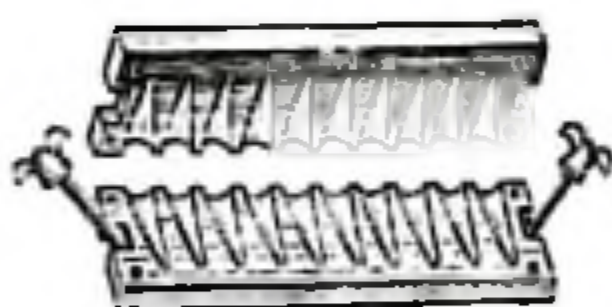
Фрезерованная форма для отливки суппозиториях
